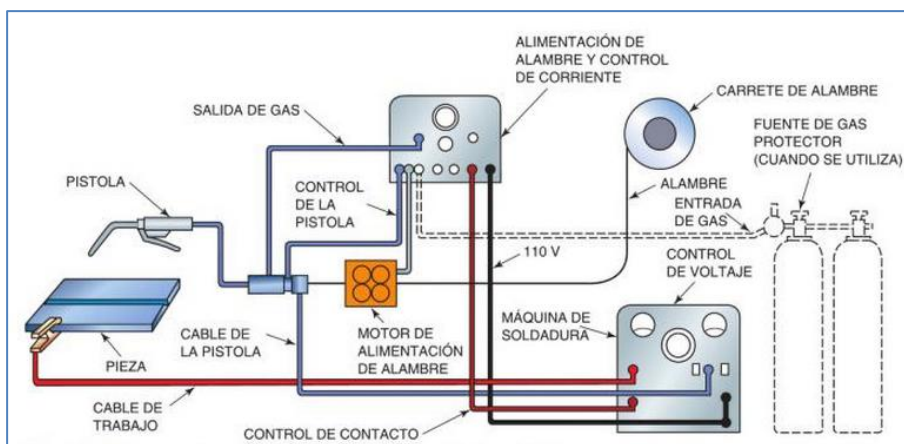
10 Esquema del equipo para soldadura por arco metálico con gas de protección (3)
